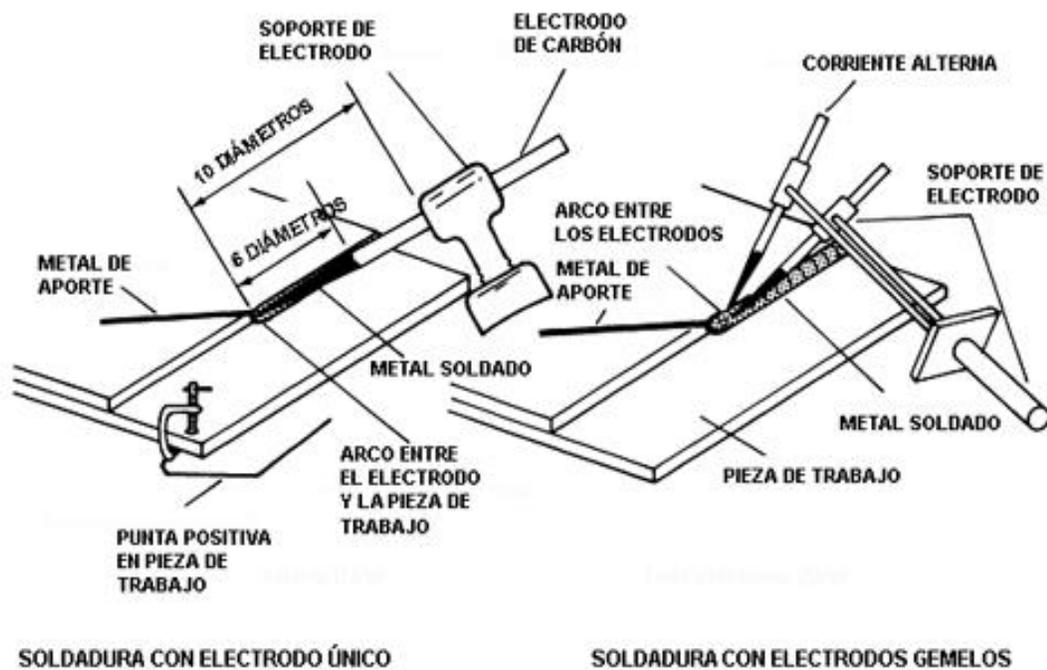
Proceso de soldadura con arco de carbón.
